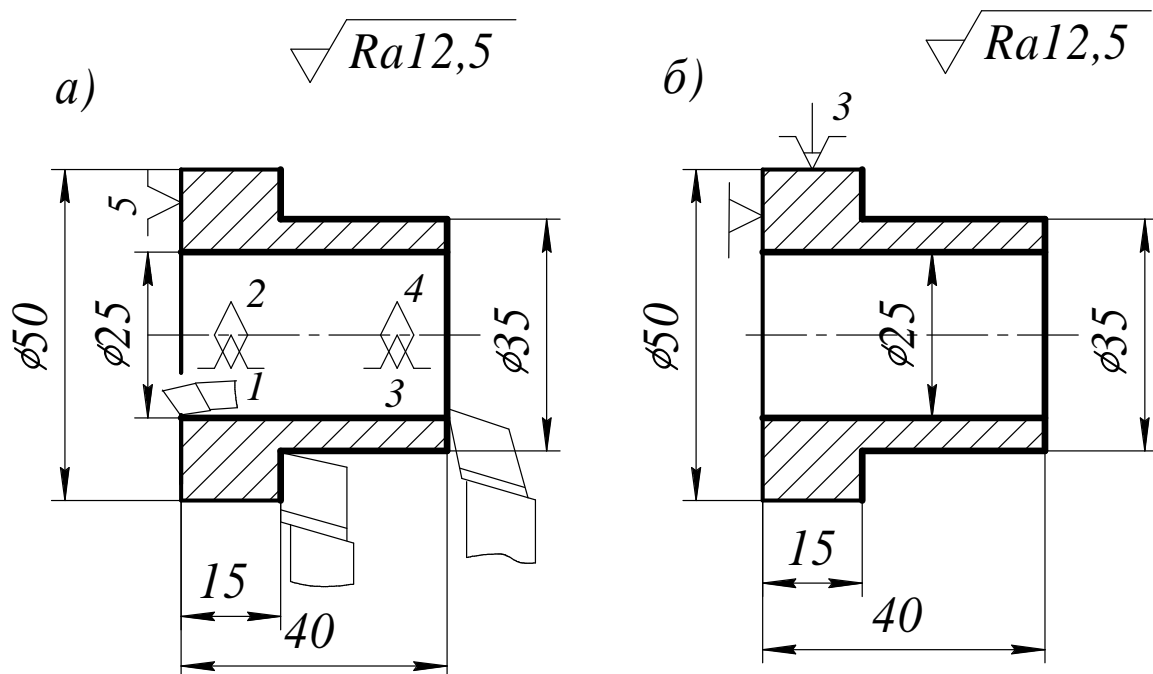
Операционный эскиз токарной операции, совмещенный с теоретической схемой базирования (а), и схема установки заготовки (б)
